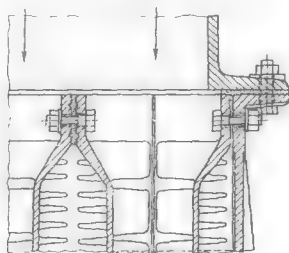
Чугунный пластинчатый воздухоподогреватель
